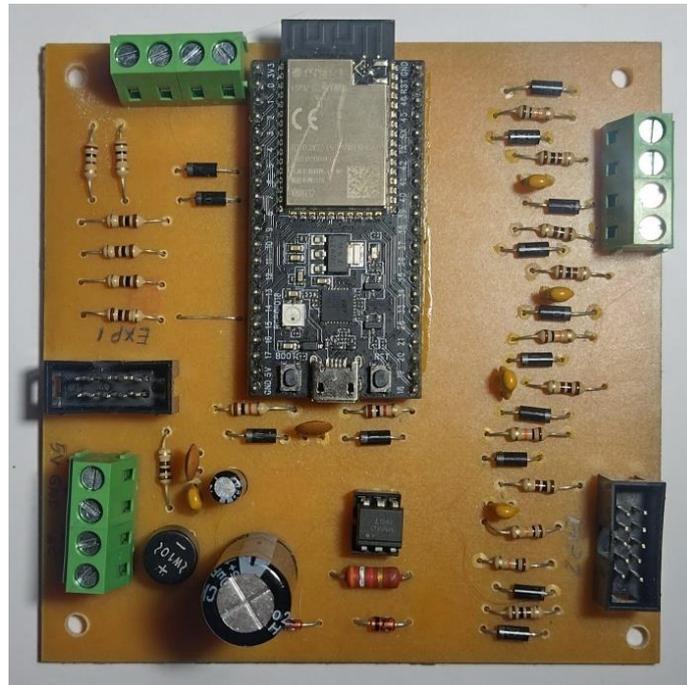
Placa PCB con los componentes montados y soldados
